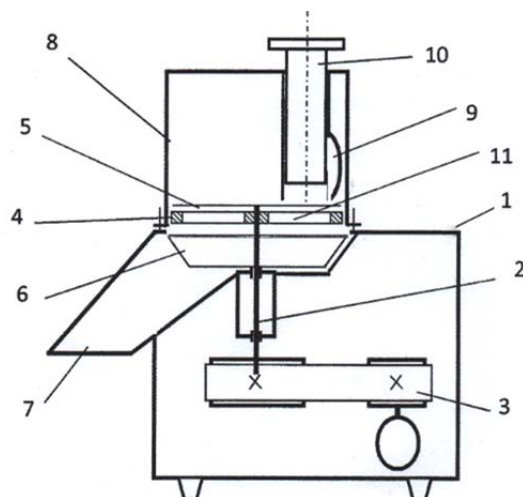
Кинематическая схема: 1 — корпус; 2 — вертикальный приводной вал; 3 — привод, состоящий из электродвигателя и клиноременной передачи; 4 — опорные диски; 5 — ножи; 6 — сбрасыватель; 7 — разгрузочное отверстие; 8 — загрузочное устройство; 9 — рабочая камера; 10 — толкатель; 11 — отверстия опорных или тёрочных дисков
